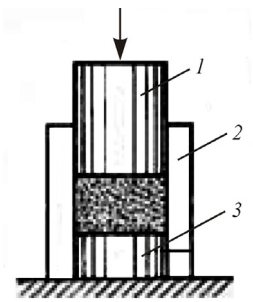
Пресс-инструмент для соосного прессования: 1 – пуансон верхний; 2 – матрица; 3 – пуансон нижний
